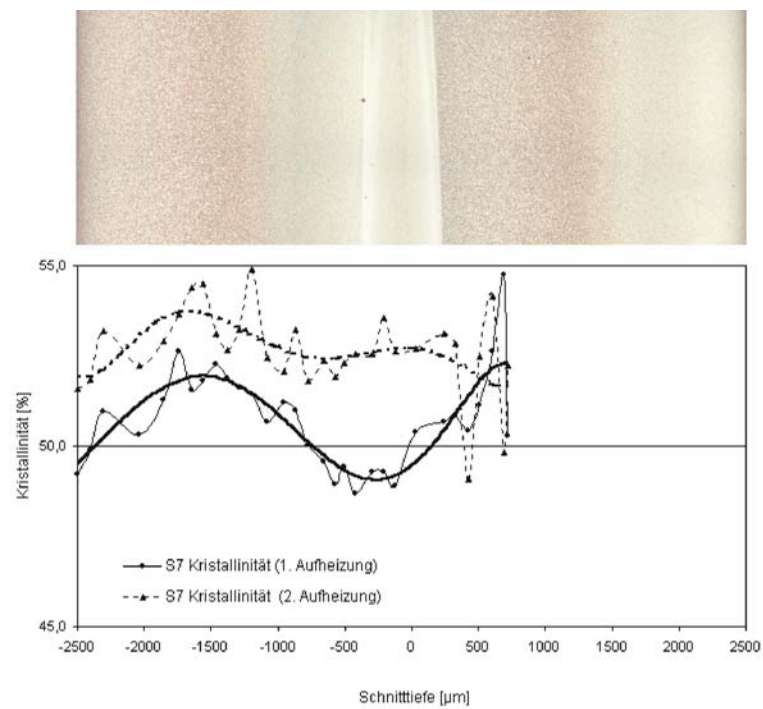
Kristallinität nach 1. und 2. Aufheizung im Querschnitt einer der Schweißnahtserie S7 entnommenen Probe mit bildhafter Zuordnung zum geätzten Querschnitt der Schweißnaht.
